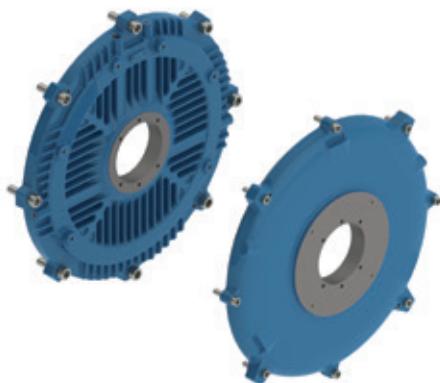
Tampa dianteira (esquerda) e tampa traseira (direita)
